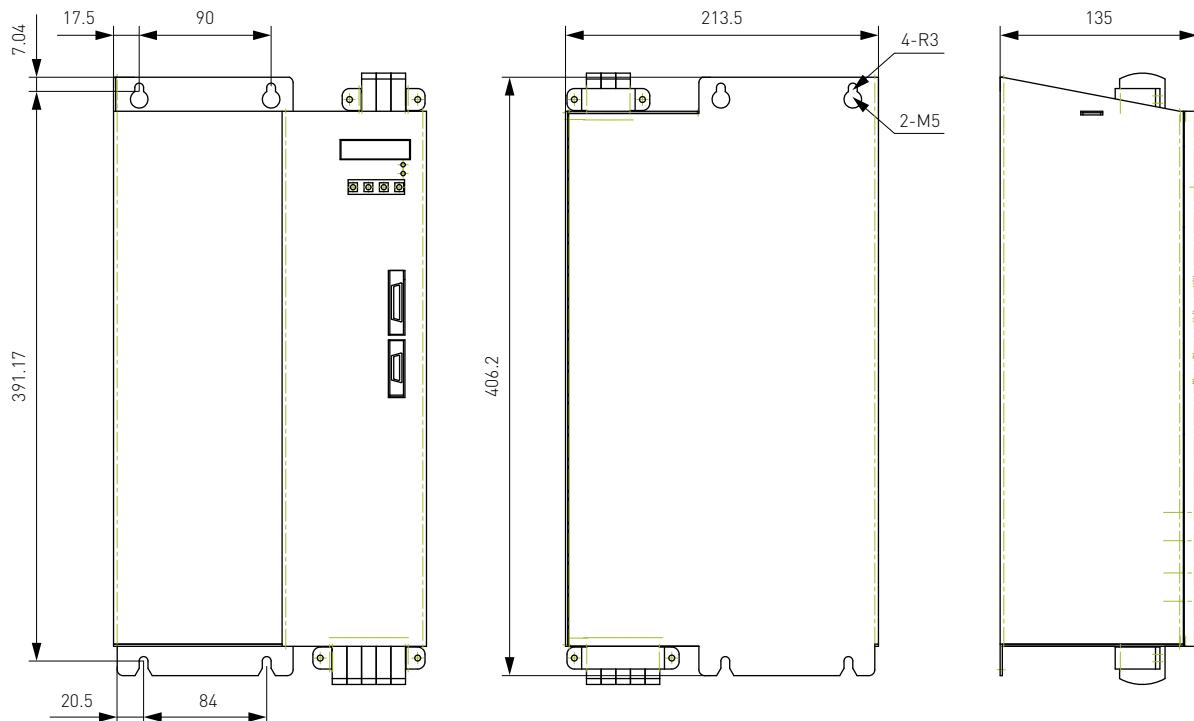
Габаритный чертеж серводрайверов A7-11KW, A7-15KW.
